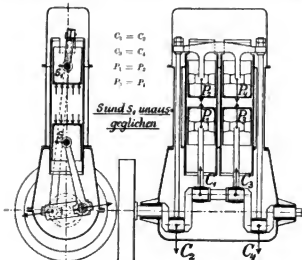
Zwilling-Balancemotor (Gobron-Brillié).
